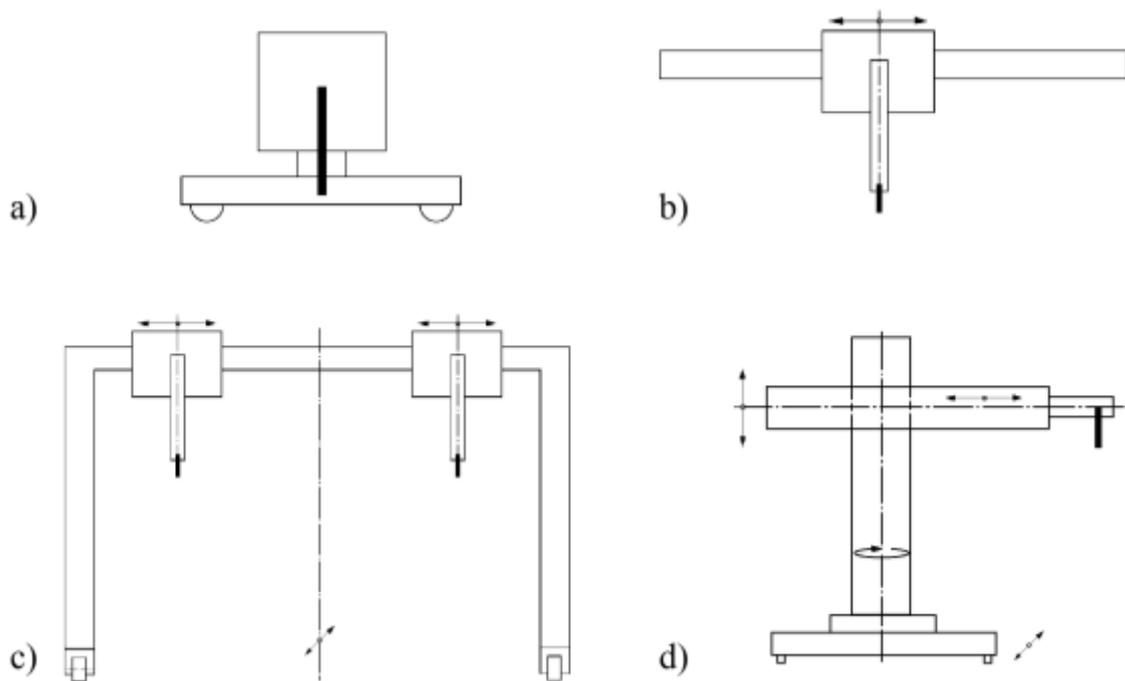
Mechanisierung der Schweißbewegung (Quelle: /38,S.191/)
